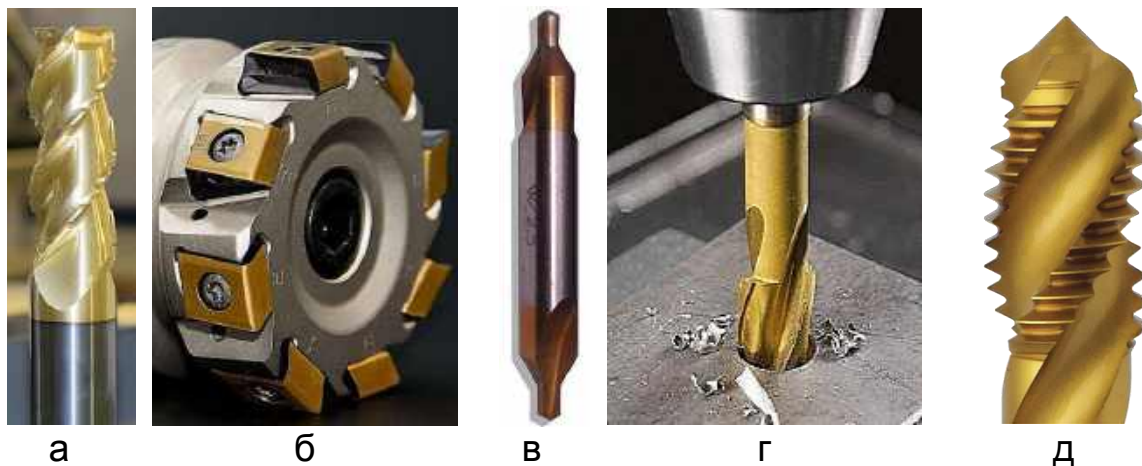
Приклади інструментів зі зносостійкими покриттями: а – кінцева фреза; б – торцева фреза з БРП; в – центрувальне свердло; г – свердло; д – мітчик
